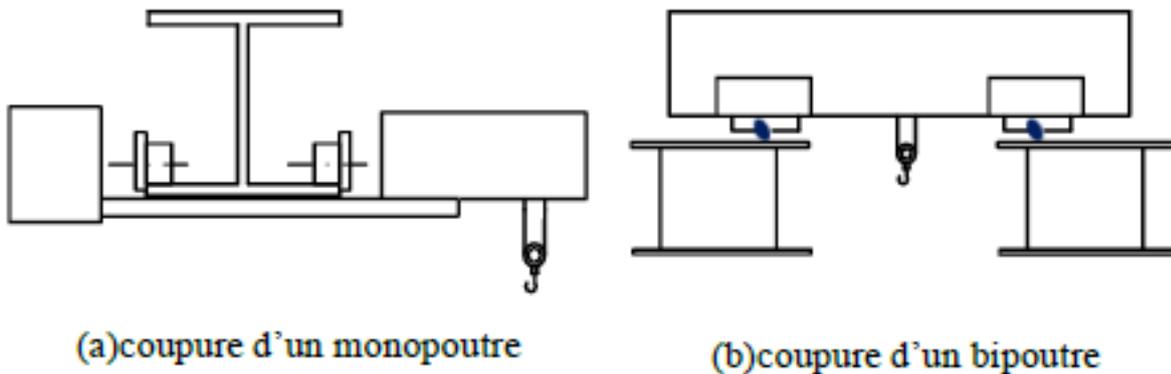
Pont roulant (a) mono poutre (b) bipoutre
